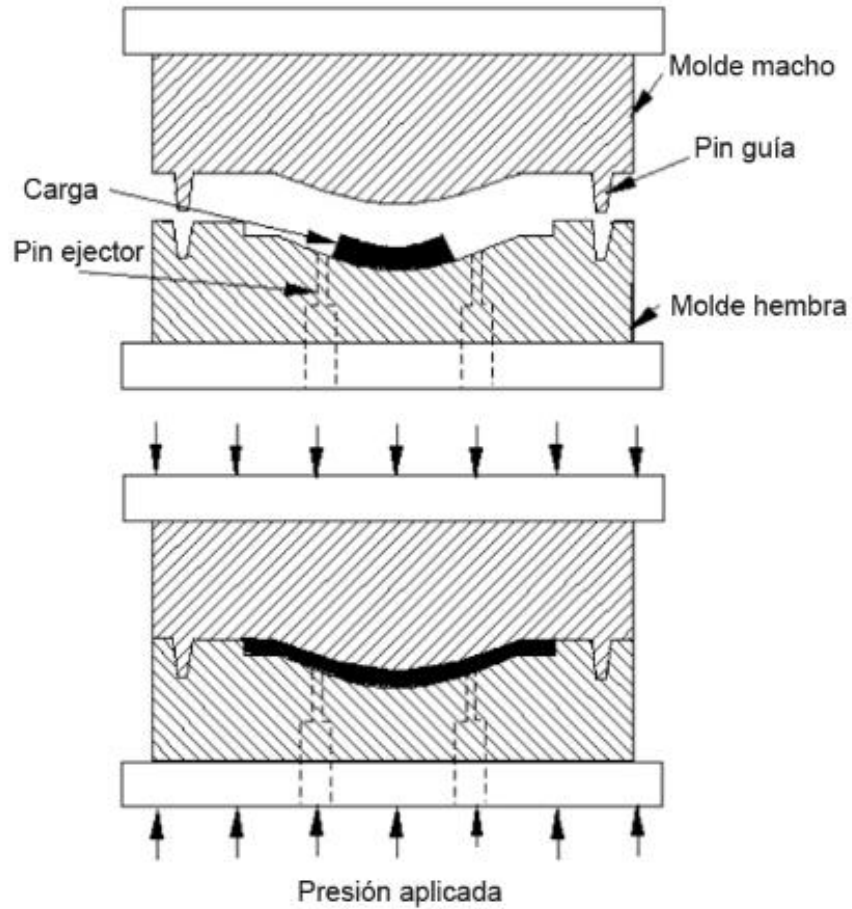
Esquema del proceso de moldeo por compresión. [11]
